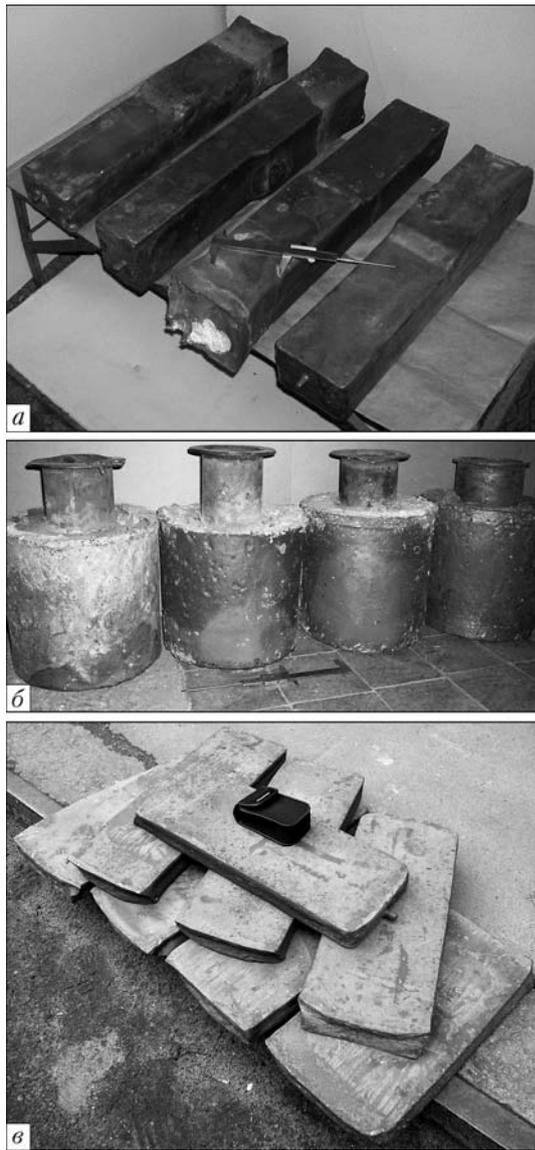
Отливки (а, б) и катаные заготовки (в) из бронзы Бр.КН1-3 электрошлаковой выплавки
